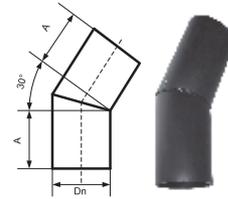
Отвод 30° сварной 2-х сегментный
